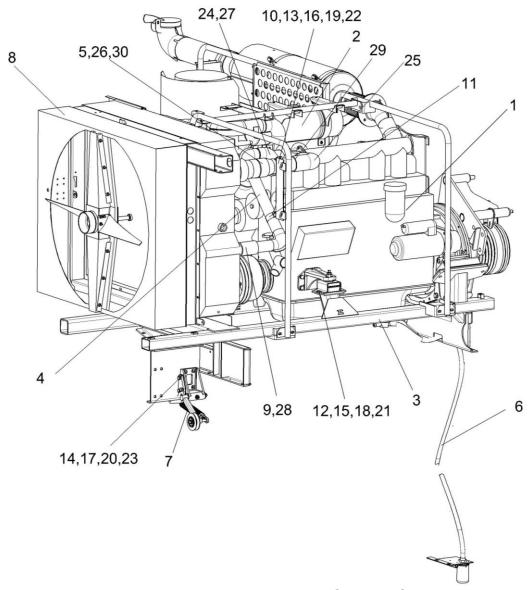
Установка двигателя Д260.7С-504 КЗК-10-1-0106000 (лист 2)
